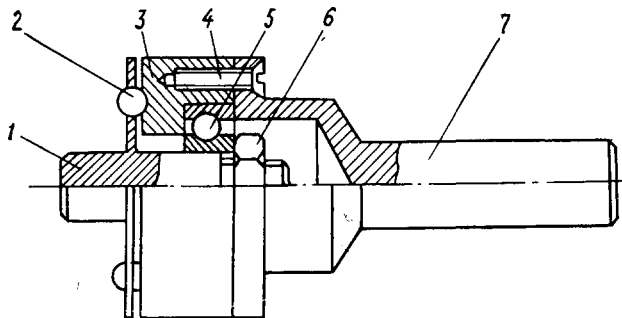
Схема оправки для машинной завальцовки подшипника:
